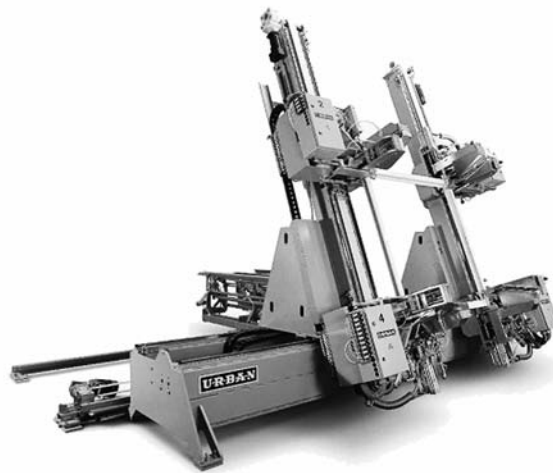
Schwenkbare 4-Kopf-Schweißmaschine zum vertikalen Einlegen der Profilschenkel
